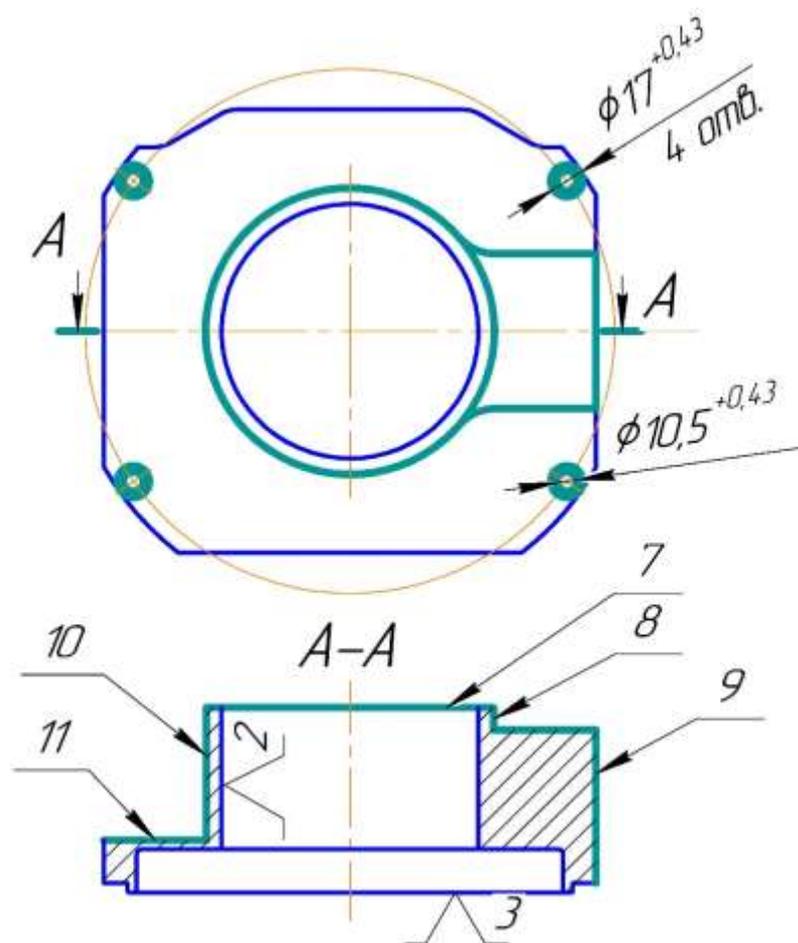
а – эскиз для фрезерной операции с ЧПУ 015.
